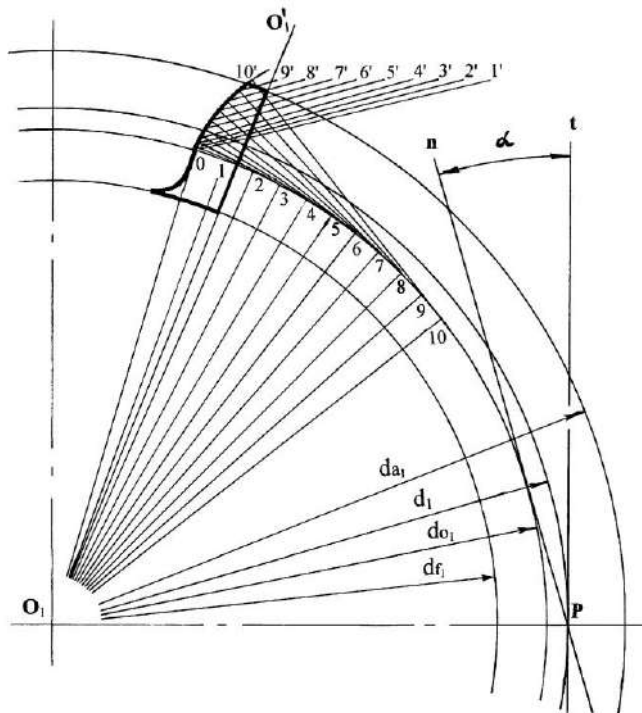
Построение эвольвентного профиля зуба первого (ведущего) колеса и шаблона зуба
